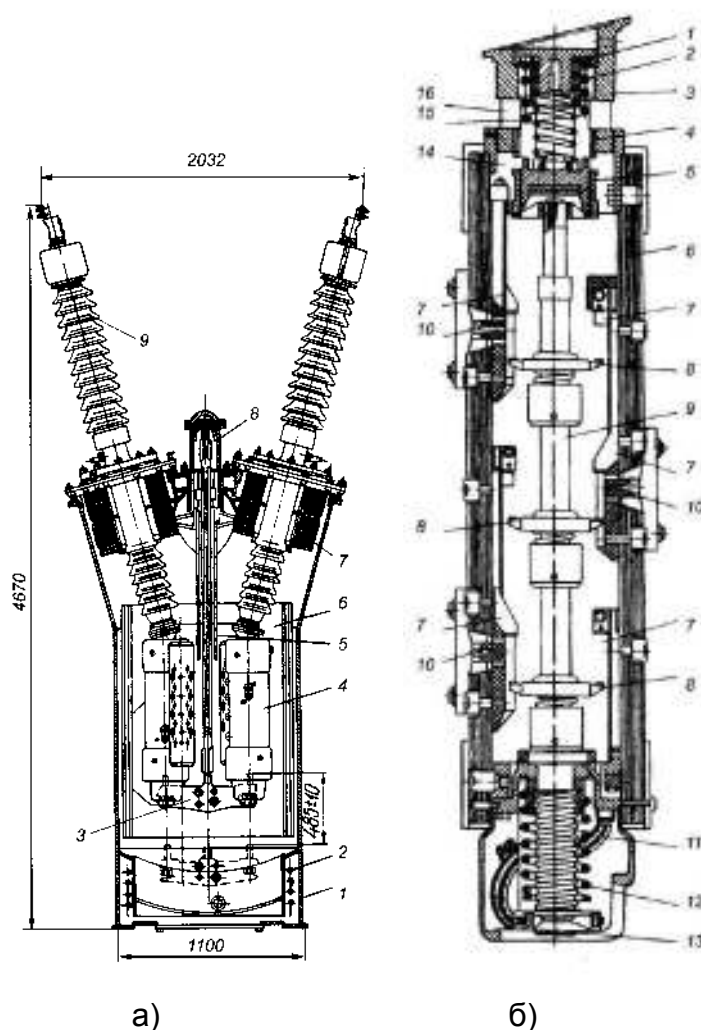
выключатель У-220: а) полюс трёхбакового масляного выключателя У-220-40: 1 – бак; 2 – трубчатые нагреватели; 3 – траверса; 4 – дугогасительное устройство с шунтом; 5 – направляющее устройство; 6 – изоляция бака; 7 – трансформаторы тока; 8 – механизм выключателя; 9 – маслонаполненный ввод; б) дугогасительное устройство выключателя У-220-40
